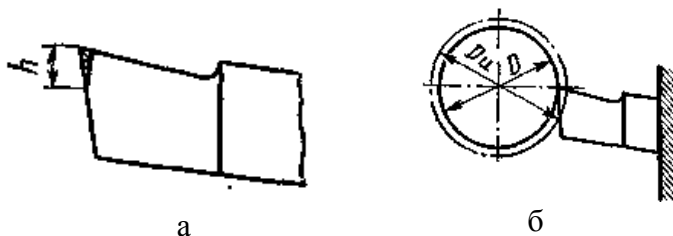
Спрацювання інструмента та його вплив на геометрію обробленої поверхні: а – затуплення різальної кромки інструмента; б – вплив затуплення інструмента на діаметральні розміри обробленої поверхні
